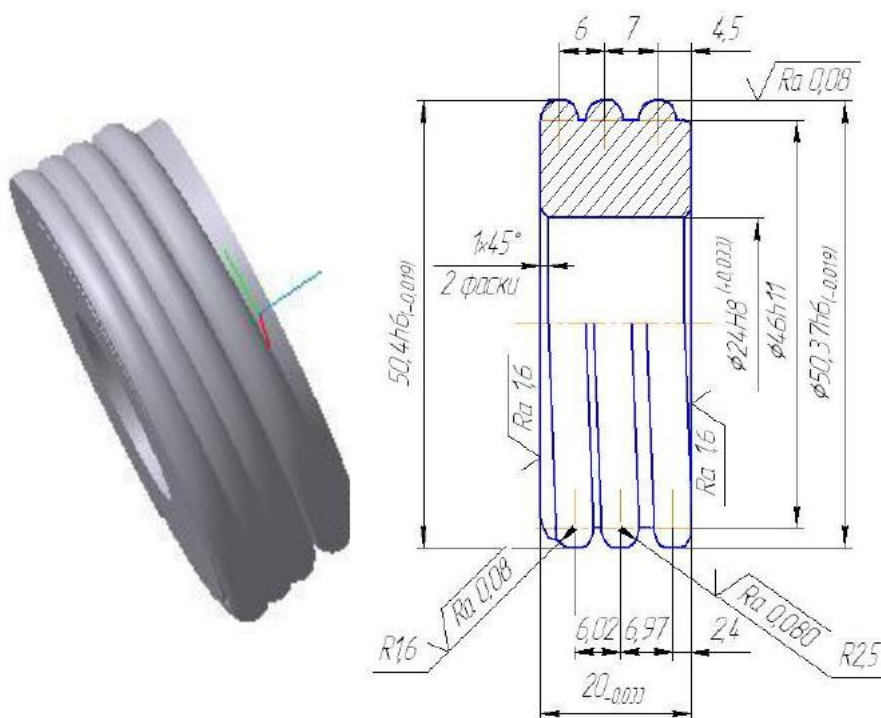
Інструмент для поверхневого пластичного деформування
